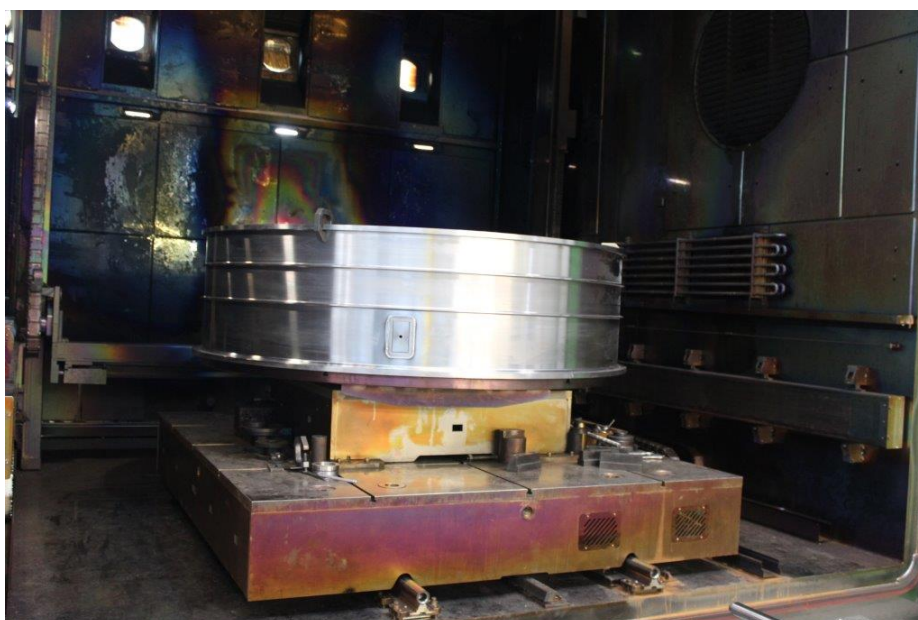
Установка ТЕТА 60Е2500 ЭЛС ДСЕ корпус компрессора
